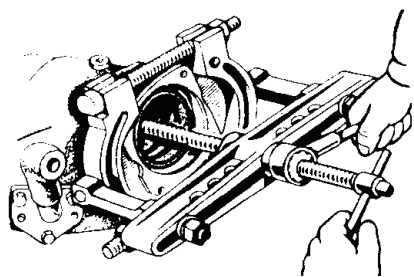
Выпрессовка гильзы шкворня из корпуса редуктора конечной передачи.
